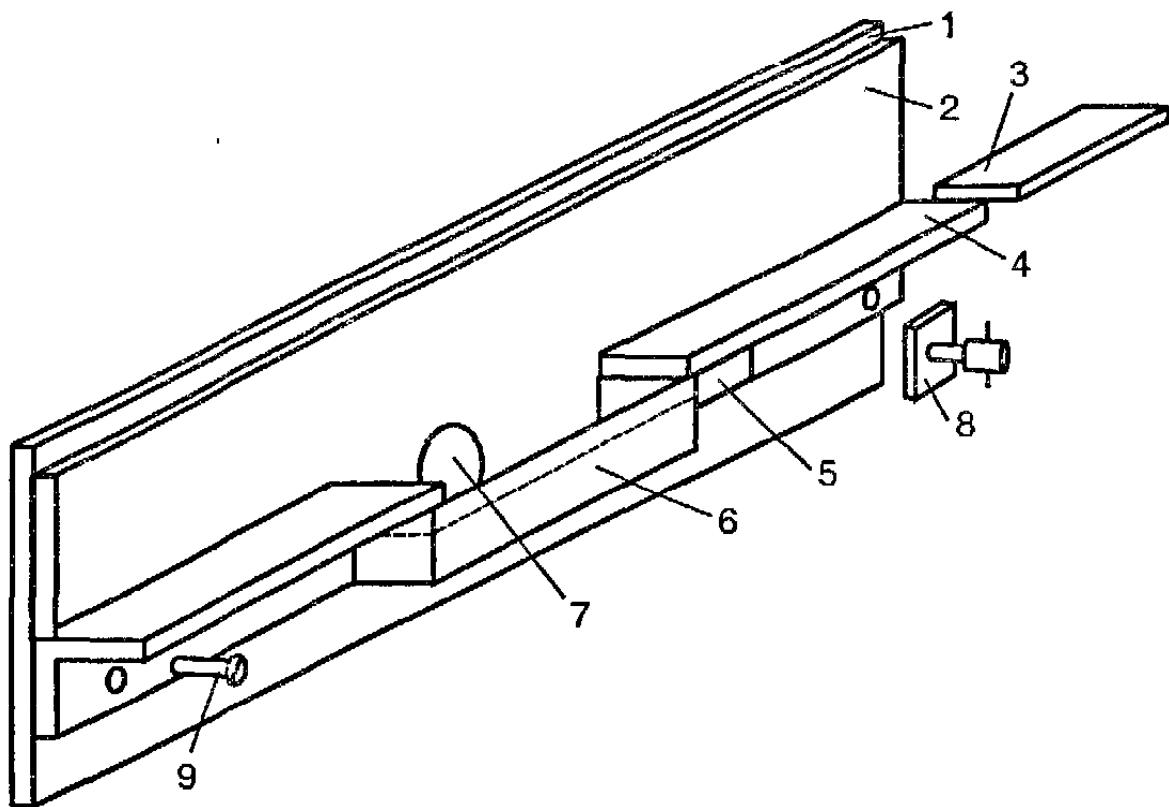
Фрезерное приспособление для третьей позиции станка:
